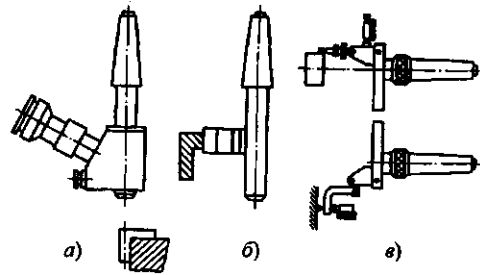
Устройства, используемые при наладке нулевого положения: а – оптическое устройство; б – контрольная оправка; в – центроискатель
